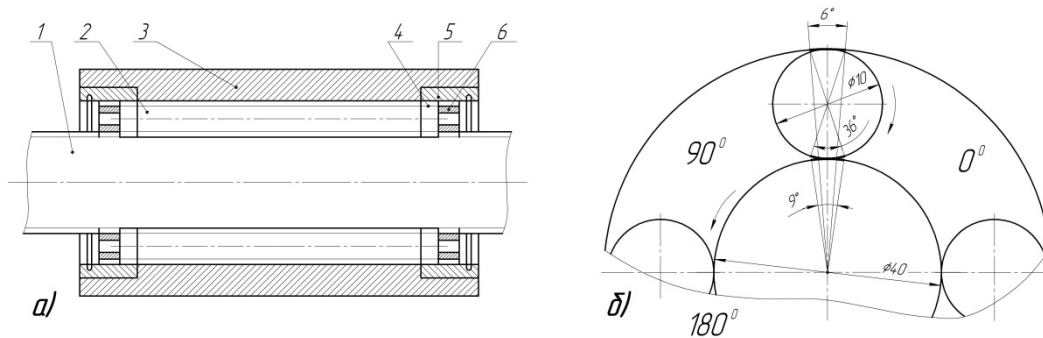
Планетарная роликвинтовая передача: а) конструкция (1– винт; 2– резьбовые ролики; 3– гайка; 4– зубчатые венцы ролика; 5– зубчатые венцы гайки; 6– сепаратор); б) геометрическая схема соотношения углов поворота элементов передачи.
